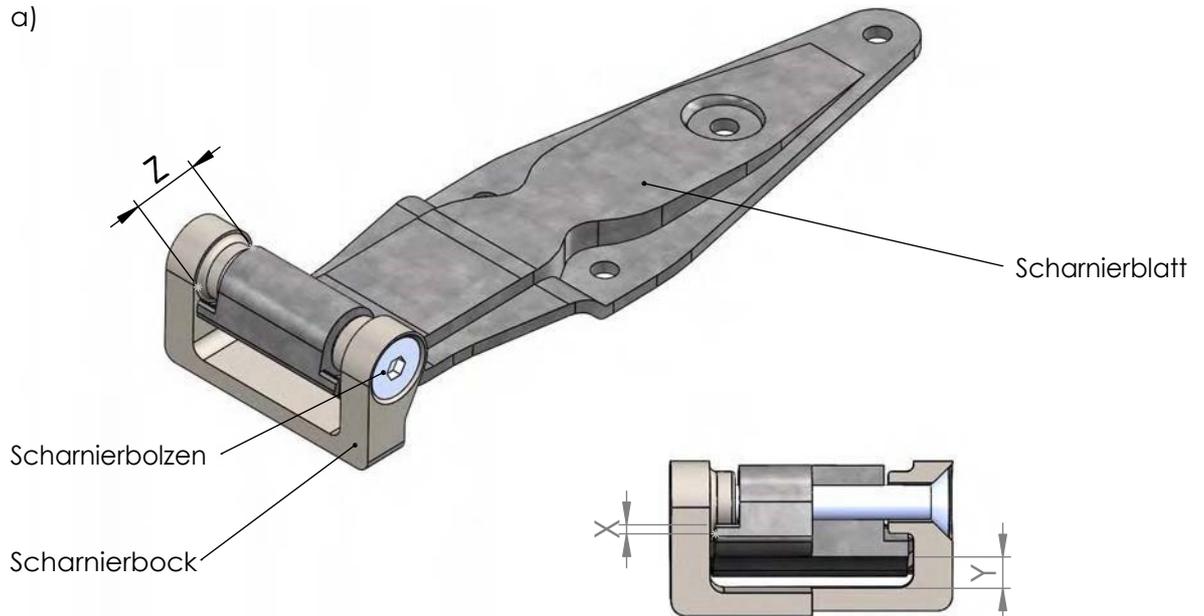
Sicherung des Scharnierbolzens (verschweißt)
